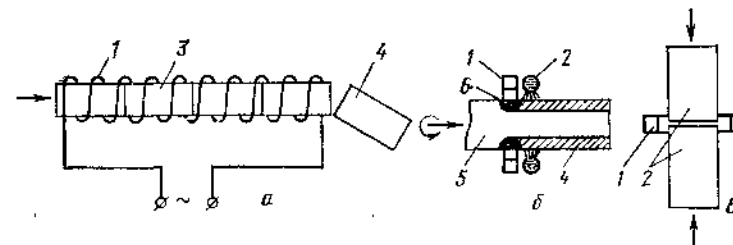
Установки для индукционного нагрева: а — сквозной нагрев под пластическую деформацию и термообработку (1 — индуктор; 3 — нагреваемая заготовка; 4 — нагретая заготовка); б — поверхностная закалка (1 — индуктор; 2 — спрей; 4 — закаленная зона; 5 — закаливаемая деталь; 6 — нагреваемый участок); в — сварка прутков астык (1 — индуктор; 2 — свариваемые прутки)
